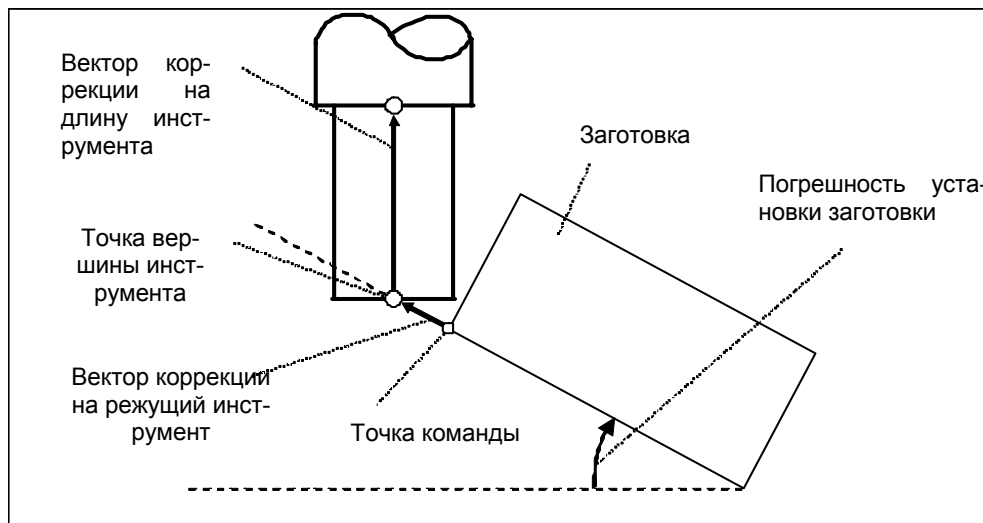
(n) Коррекция на режущий инструмент, когда имеется погрешность установки заготовки (если RCM=0)
